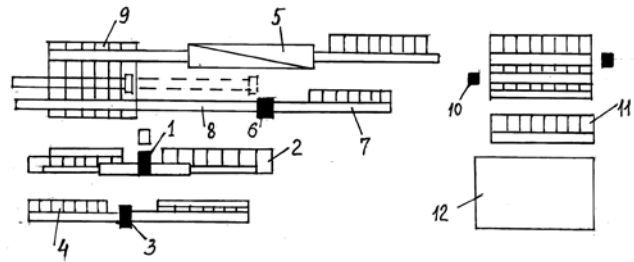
Участок отделки ГДТ: 1 – правильная машина; 2 – передаточная решетка; 3 – станок для снятия фаски и заусенцев; 4 – установка для выдувки окалины; 5 – установка дефектоскопа и измерителя длины труб; 6 – станок для клеймения труб; 7 – установка кармана с выбрасывателем; 8 – инспекционная решетка; 9 – вязальная машина; 10 – агрегатный станок для ремонта труб; 11 – трубоотрезной станок
